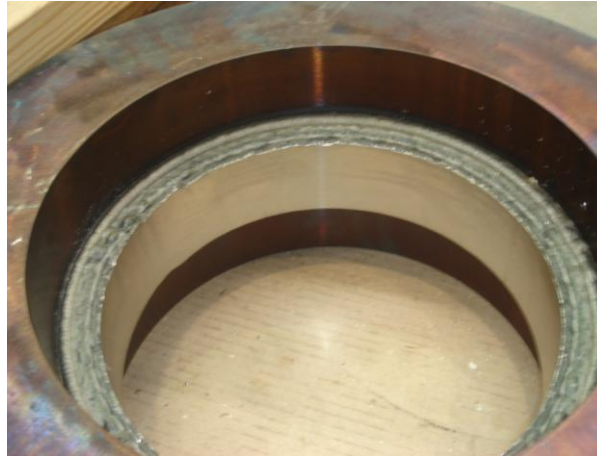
Detalhe da usinagem realizada para nivelar a 10ª camada depositada.
